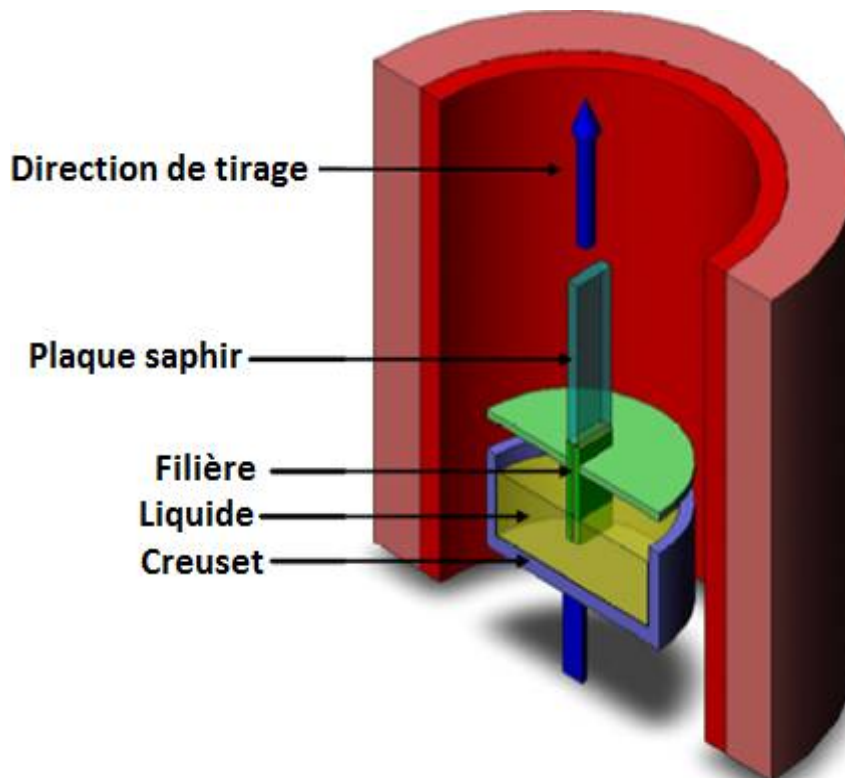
Illustration schématique du principe de méthode EFG pour une seule plaque [7].
